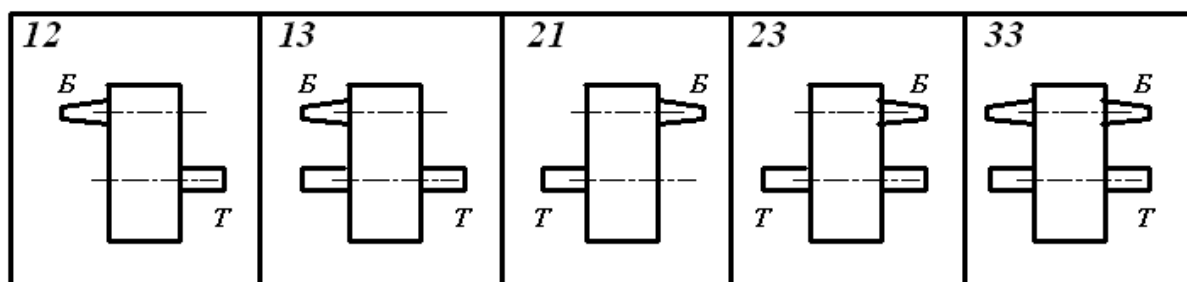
Редукторы цилиндрические вертикального исполнения
